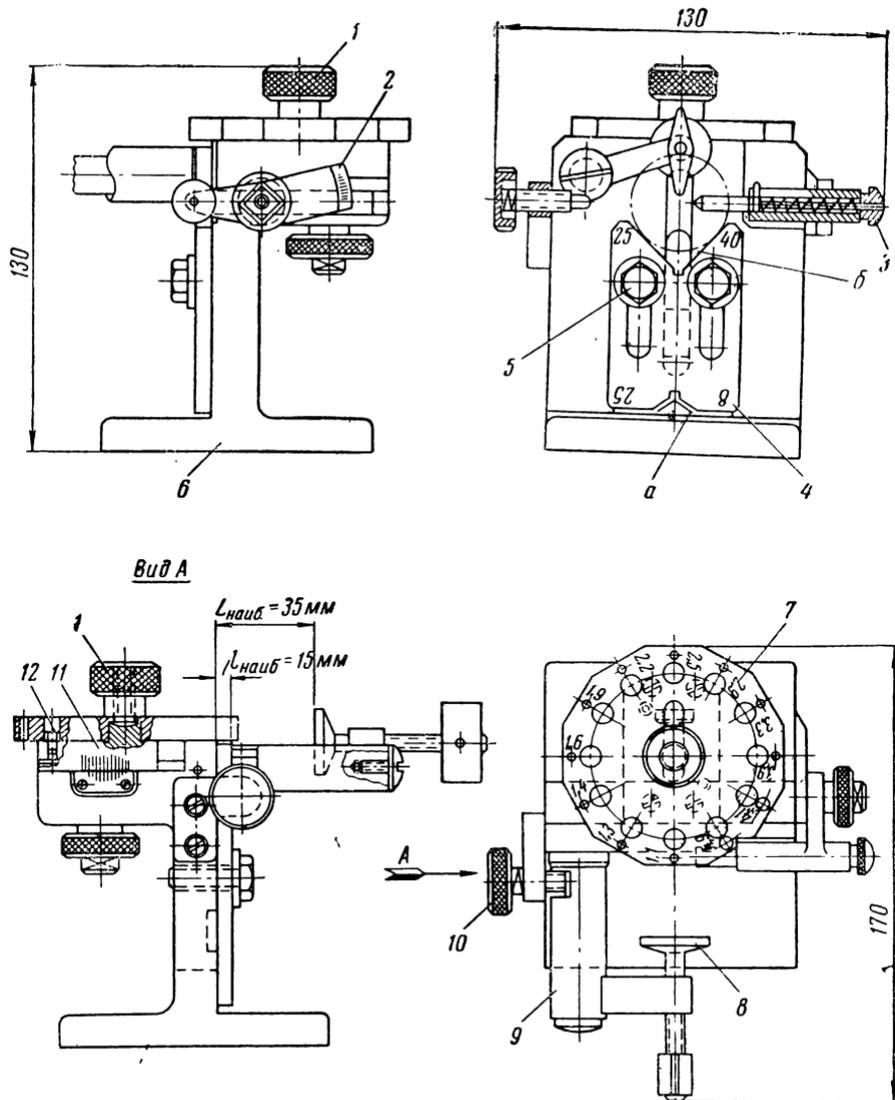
Групповой кондуктор для деталей, имеющих радиальные отверстия на цилиндрической поверхности
